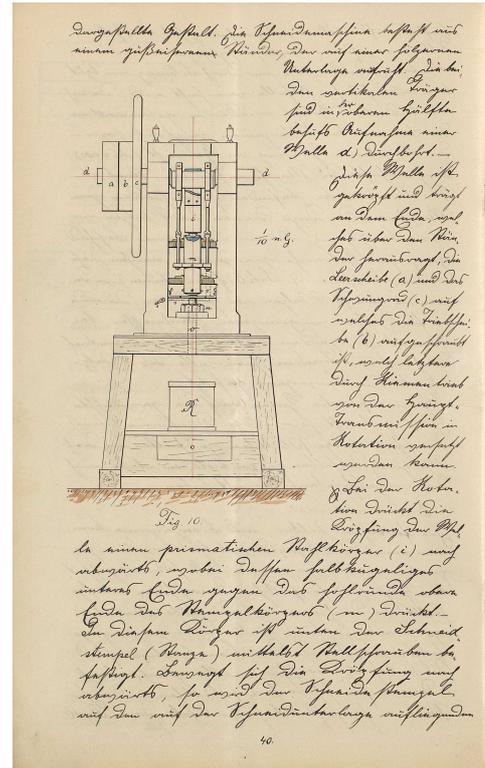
der Stanzmaschine mit genauer Beschreibung des Ablaufes.
